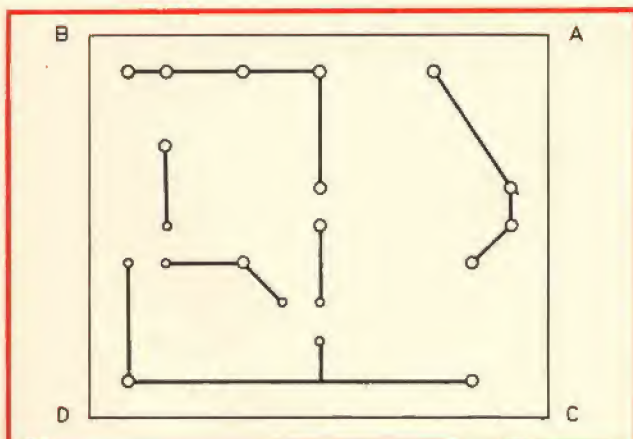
Circuito stampato del lampeggiatore visto dal lato rame.
